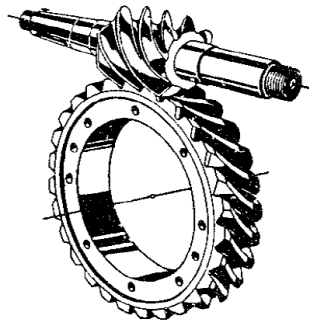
Engrenagem sem-fim/roda dentada [1].
